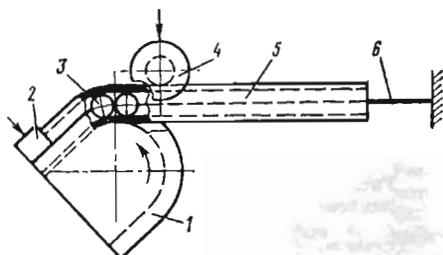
Оснастка для гибки труб на станках с поворотным столом:
